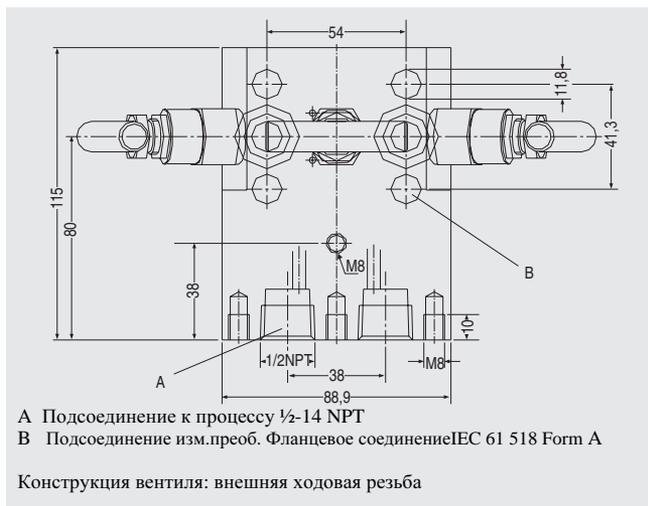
/113 Трехшпindelный вентиляльный блок DN 5, размеры
